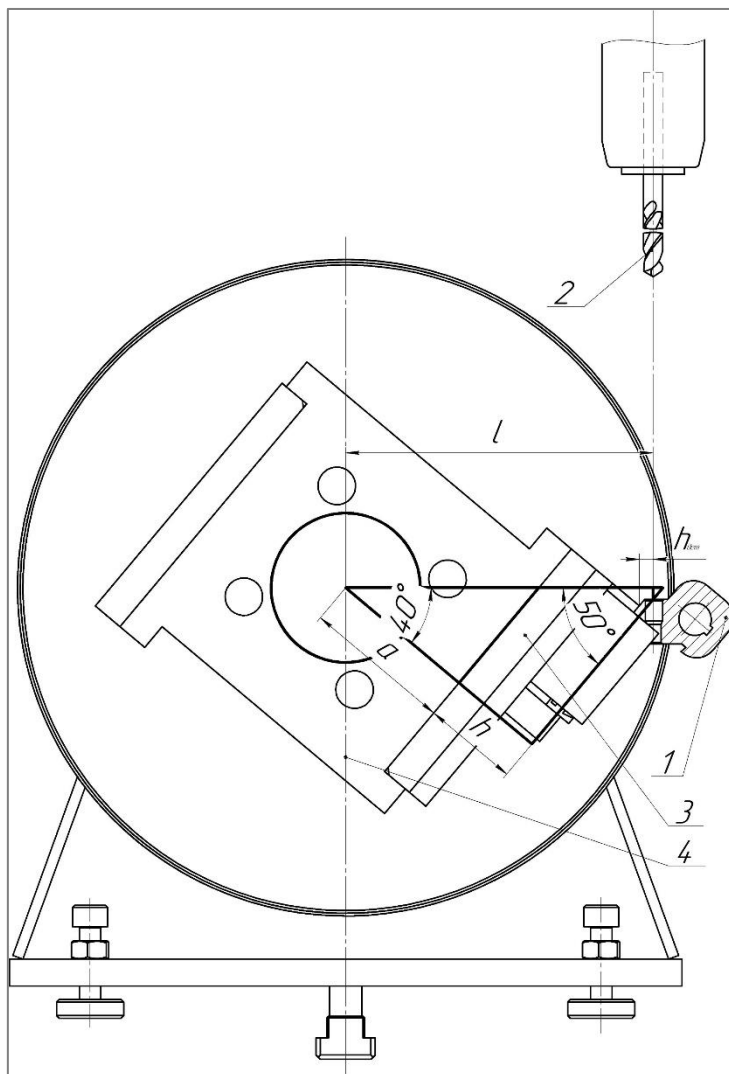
Размерная цепь для расчета допусков приспособления
